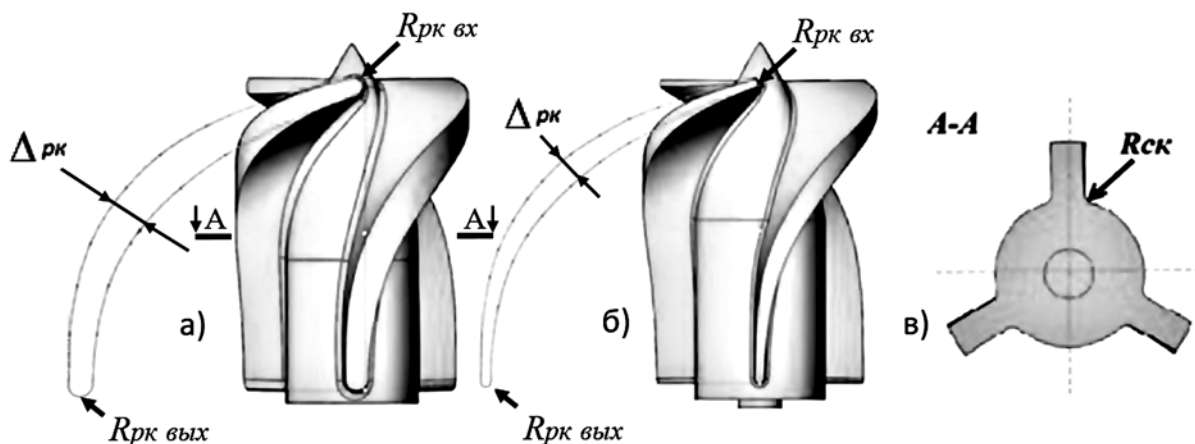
Рабочие колеса, изготовленные из пластика (а); из медстали (б); сечение пластикового РК (в)
